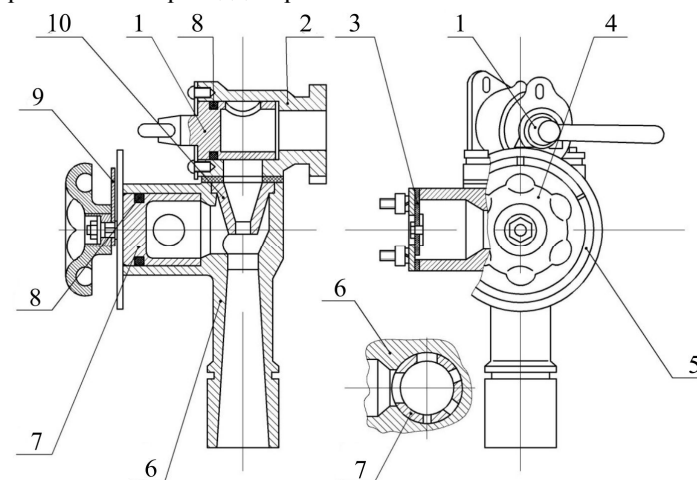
Стаціонарний пінозмішувач ПЗ-5: 1) корок крана пінозмішувача; 2) корпус крана пінозмішувача; 3) зворотний клапан; 4) маховичок дозатора (ручка); 5) шкала; 6) корпус (дифузор); 7) дозатор; 8) кільце ущільнювача; 9) стрілка; 10) сопло
